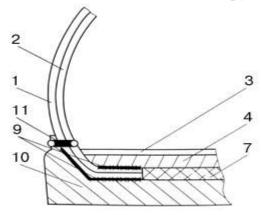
Клеево-прошивной метод крепления низа: 1 — верх обуви, 2 — подкладка, 3 — вкладная стелька, 4 — стелька (основная), 7 — простилка, 9 — клеевой шов, 10 — подошва, 11 — ниточный шов
